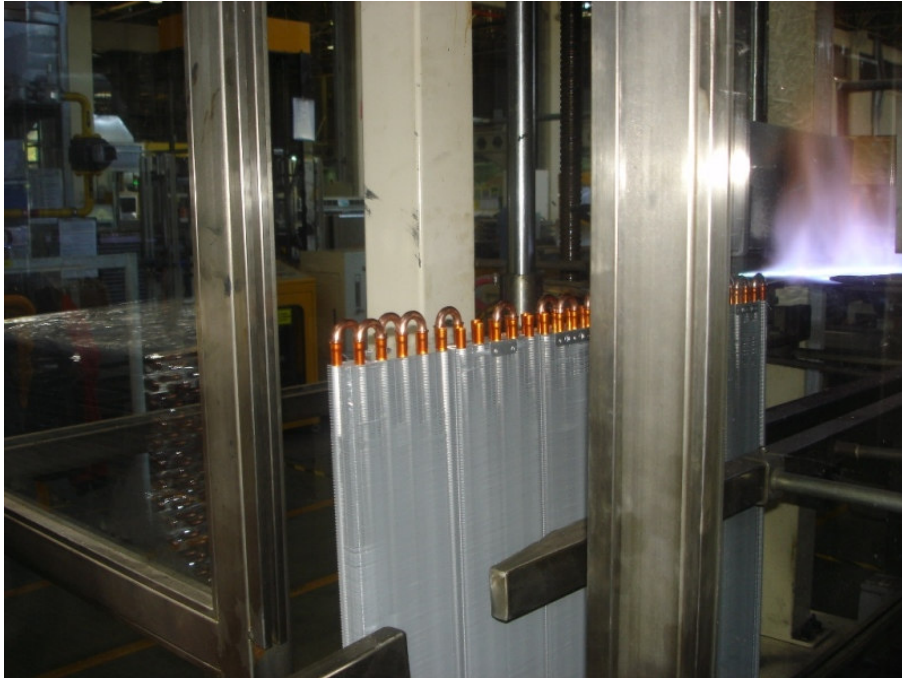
C şekilli bakır boruların U şekilli bakır borulara otomatik lehimleme öncesi montajı
